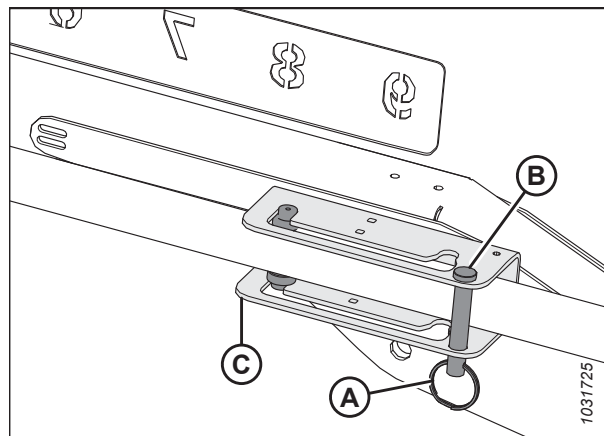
Réglage des vérins avant-arrière de type 2 – Position avant
